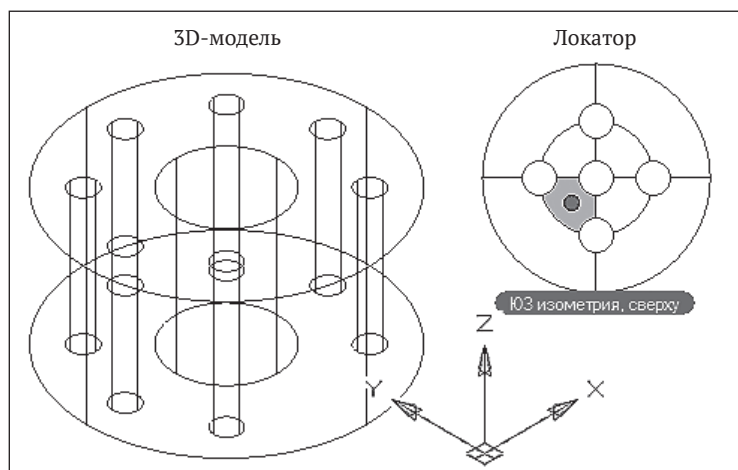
Промежуточный вид 3D-модели детали «Корпус»
